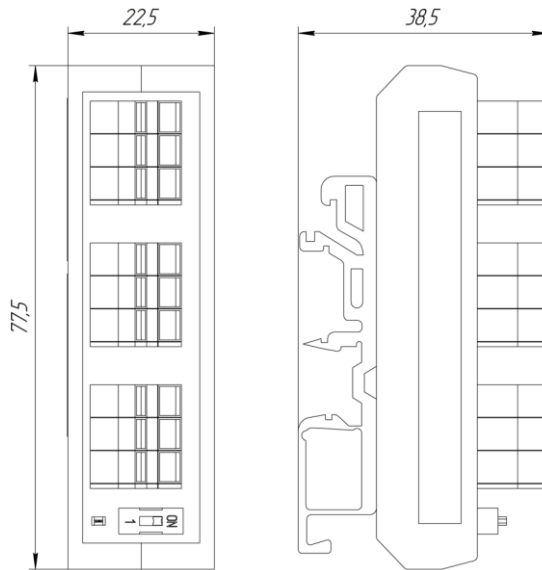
Габаритный чертеж разветвителя RS-SPLIT-3P
